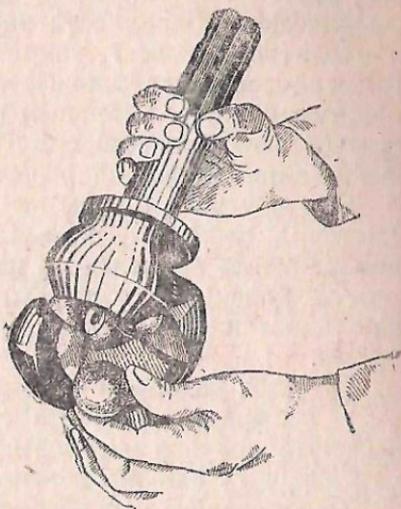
Сборка карданного шарнира „Бендикс-Вейс“
